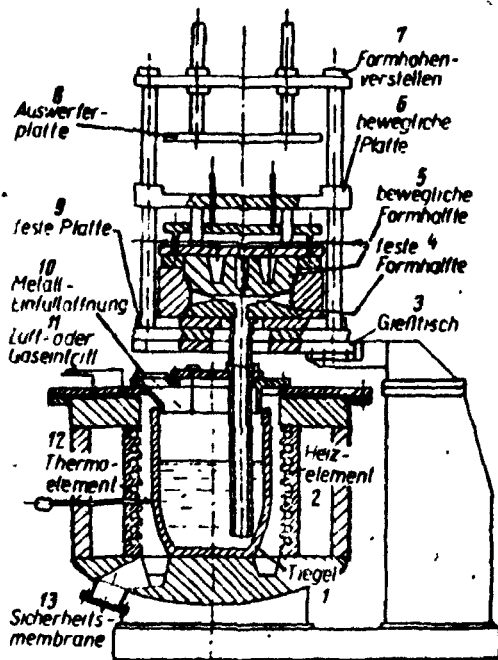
Схема и общий вид установки литья под низким давлением.
